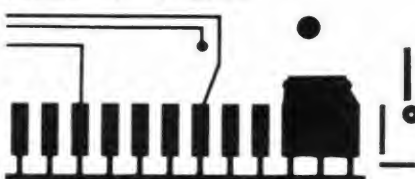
Pour que le chimique de découplage d'UVP09 serve à quelque chose.
